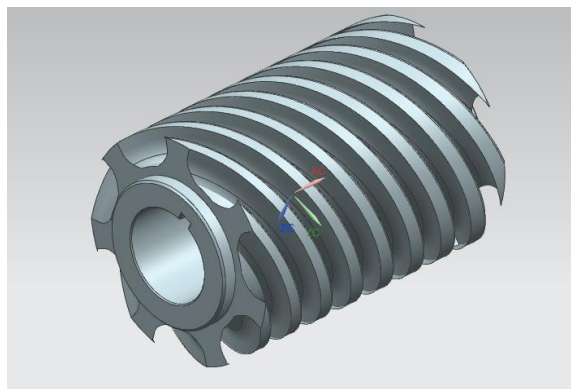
Модель инструмента червячного типа со сплошными винтовыми режущими кромками
